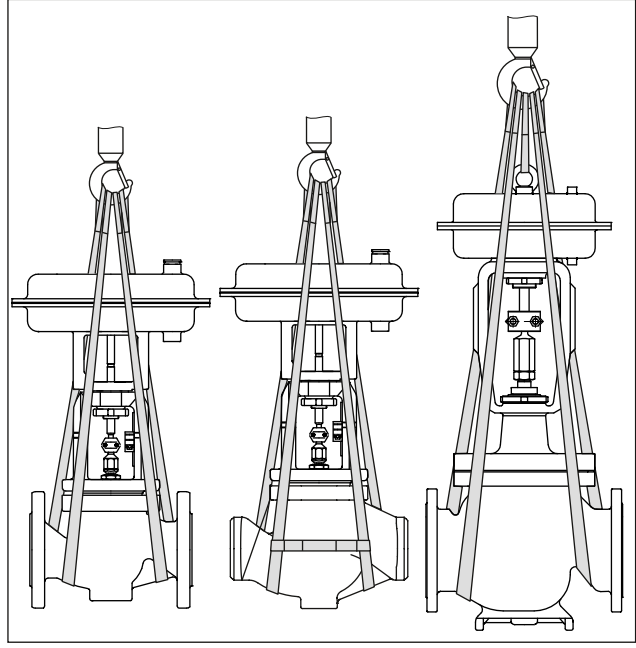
Kontrol vanası üzerindeki kaldırma noktaları: DN 150/NPS 6'ya kadar flanşlı (solda) ve kaynak uçlu (ortada) · DN 150/NPS 6 ve daha büyük tahrik ünitesi üzerinde ek kaldırma deliğiyle (sağda)
